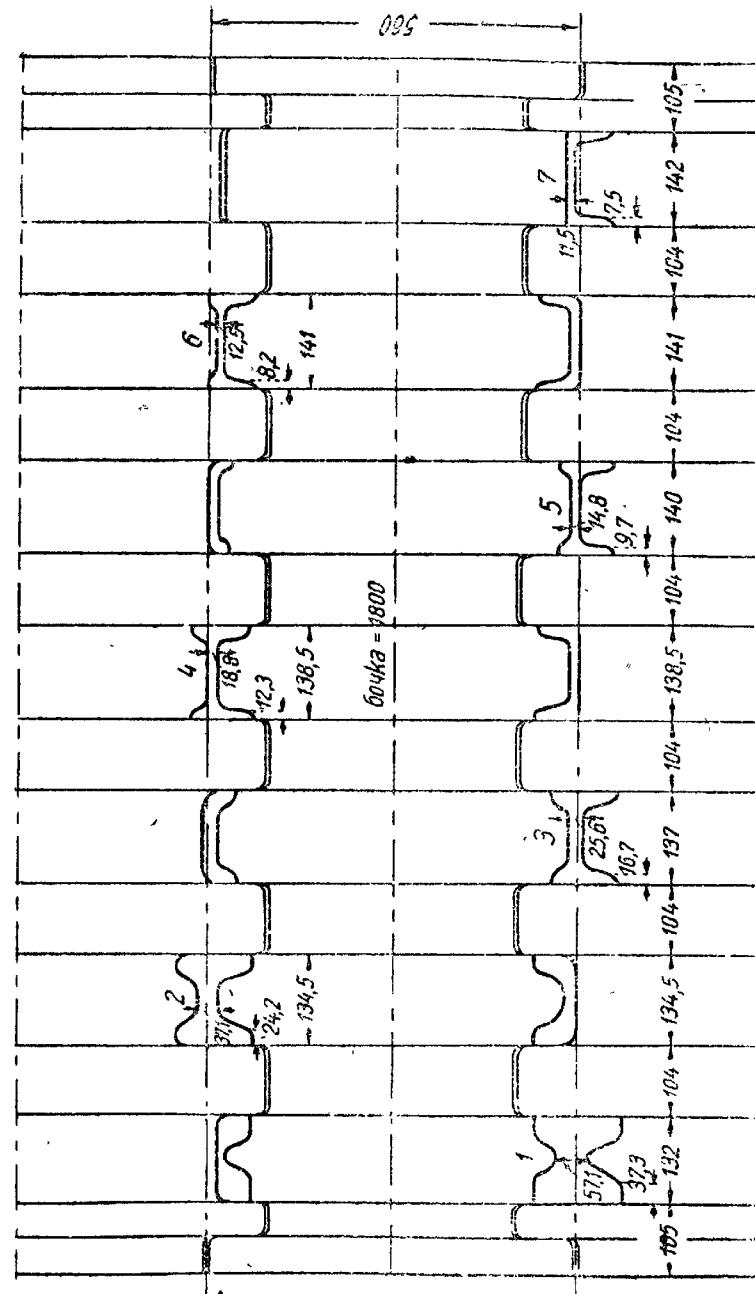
Калибрюска швейлера № 14—140 × 60 × 7 × 10⁵. Расположение отверстий в балке
